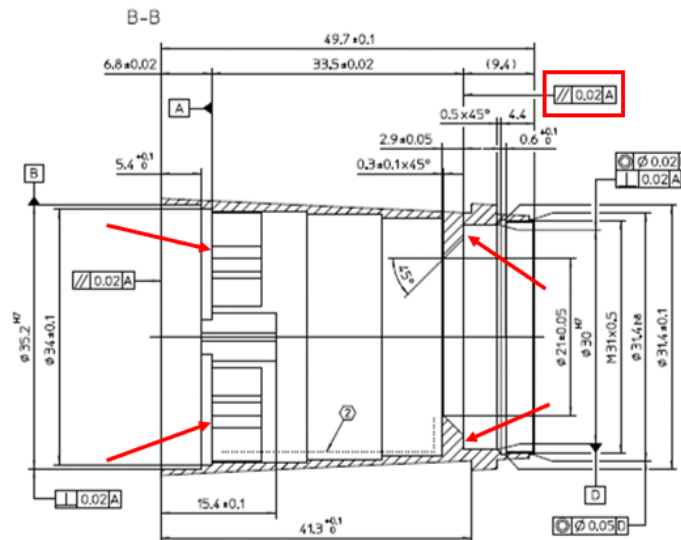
Pormenor do desenho técnico do corpo do binóculo.
